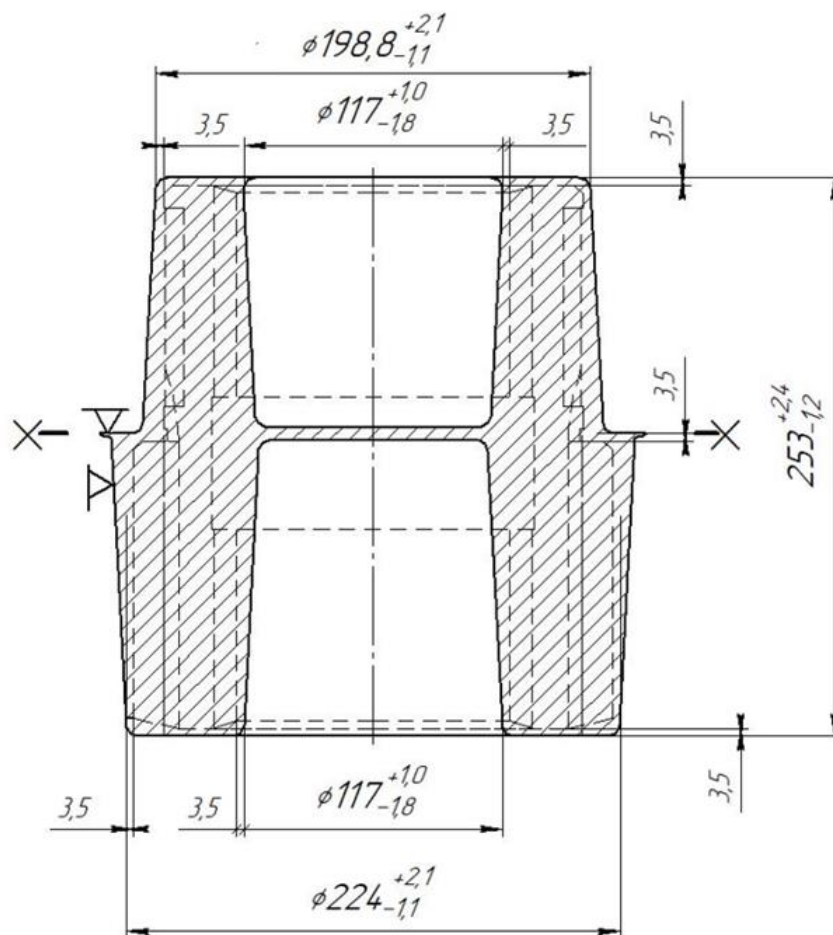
Ескіз поковки на КГШП деталі “Шестірня”
